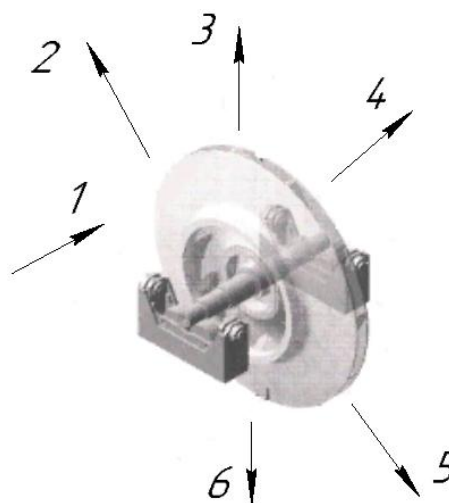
Схема расположения векторов дисбалансов рабочего колеса:
